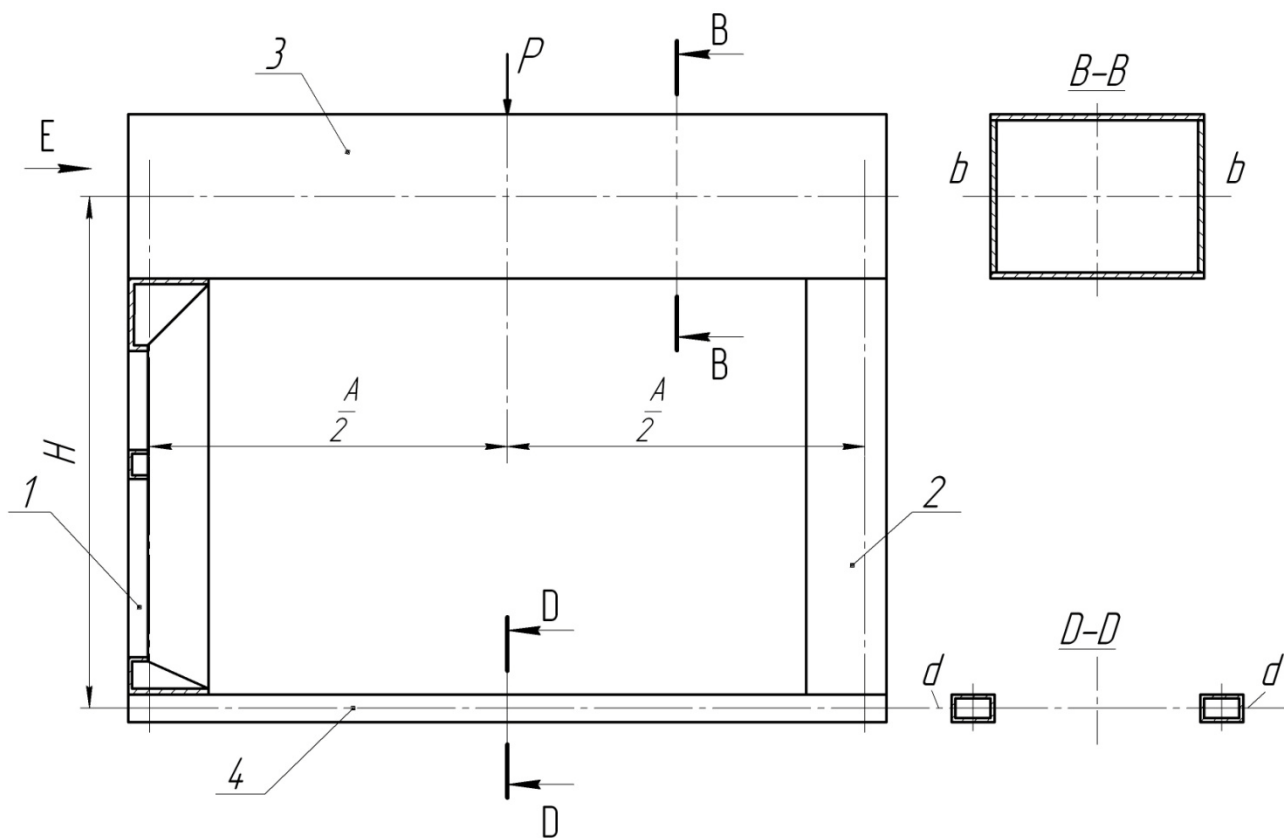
Рамная конструкция станины вырубочного прессы ПВГ-18-2-О:
